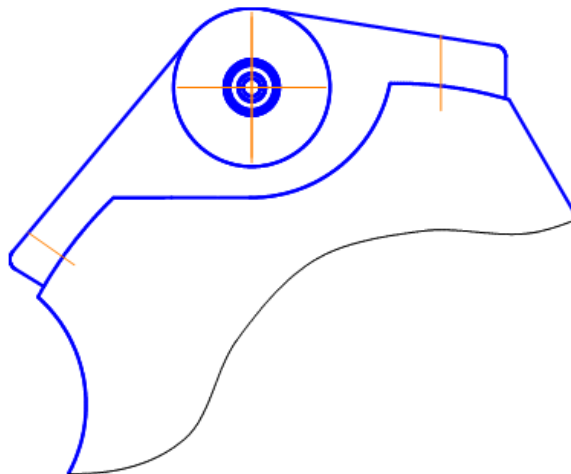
Схема крепления инструментального блока на револьверной головке, вид спереди
